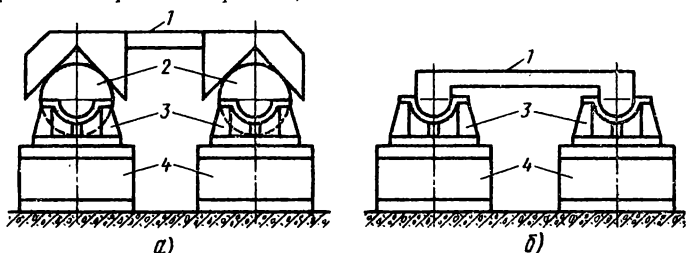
Установка роликов рольгангов с индивидуальным приводом: а — с помощью шаблона, накладываемого на бочки роликов; б — с помощью шаблона, накладываемого в расточки для подшипников; 1 — шаблоны; 2 — бочки роликов; 3 — корпуса подшипников; 4 — рамы
